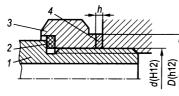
Уплотнение трубопроводов плоскими прокладками:
